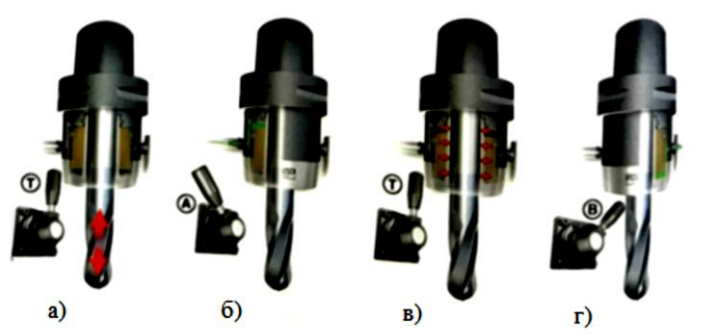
Положение рукоятки золотника при зажиме гидромеханического патрона: а – рукоятка золотника в положении Т при установке в патрон и перемещении инструмента; б – подача давления в полость цилиндра для зажима инструмента (рукоятка золотника в положении А); в – рукоятка золотника в положении Т после закрепления инструмента; г – подача давления в противоположную полость цилиндра для разжима инструмента (рукоятка золотника в положении Б).
